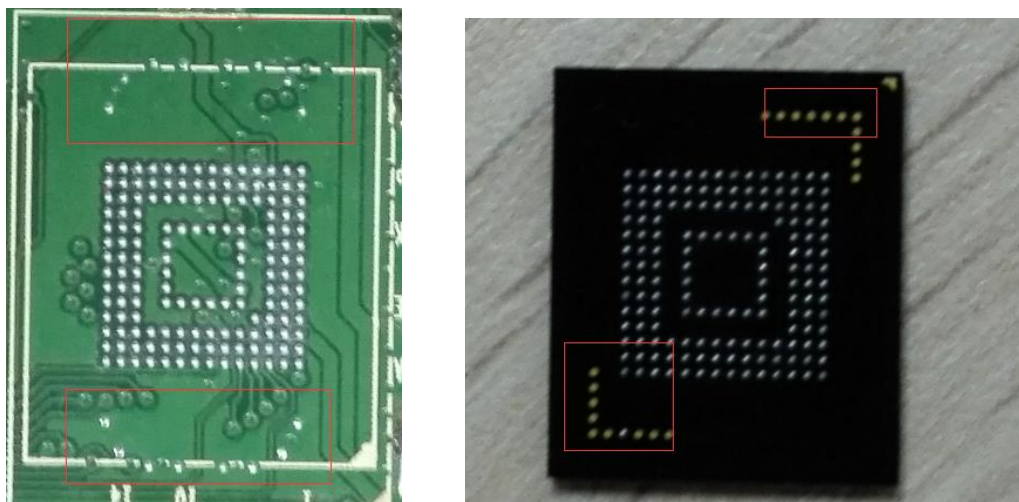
PCBA 焊盘定位脚和 flash 的测试点
